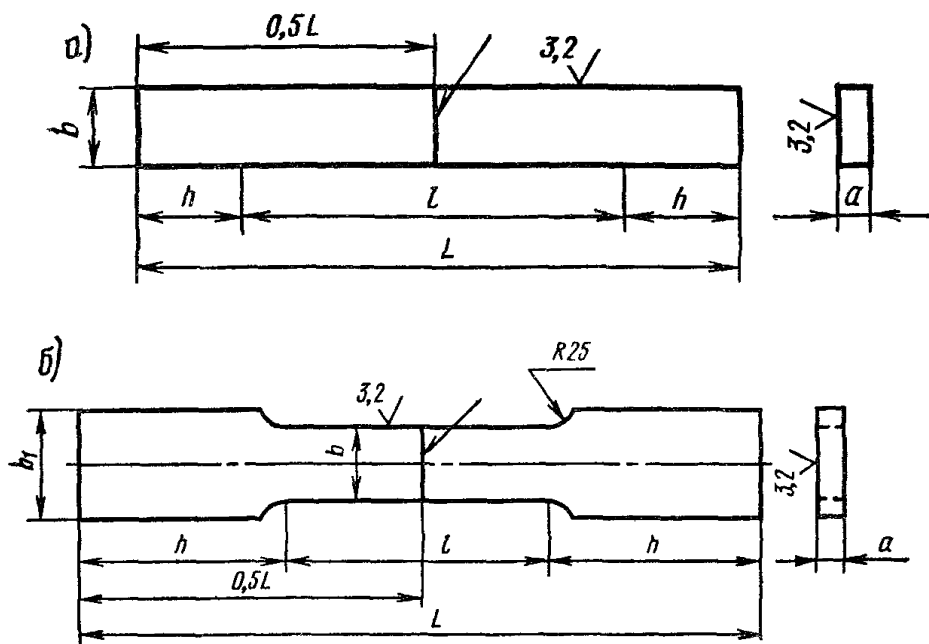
Образцы для определения равнопрочности сварного соединения при растяжении:
